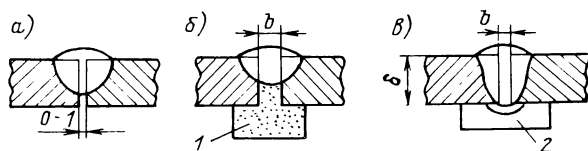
Способы формирования шва при сварке стыковых соединений: а — сварка двухсторонним швом с выполнением первого прохода на весу; б — сварка двухсторонним швом с выполнением первого прохода на флюсовой подушке; в — односторонний шов с формированием обратного вала на подкладке (медной, керамической).
